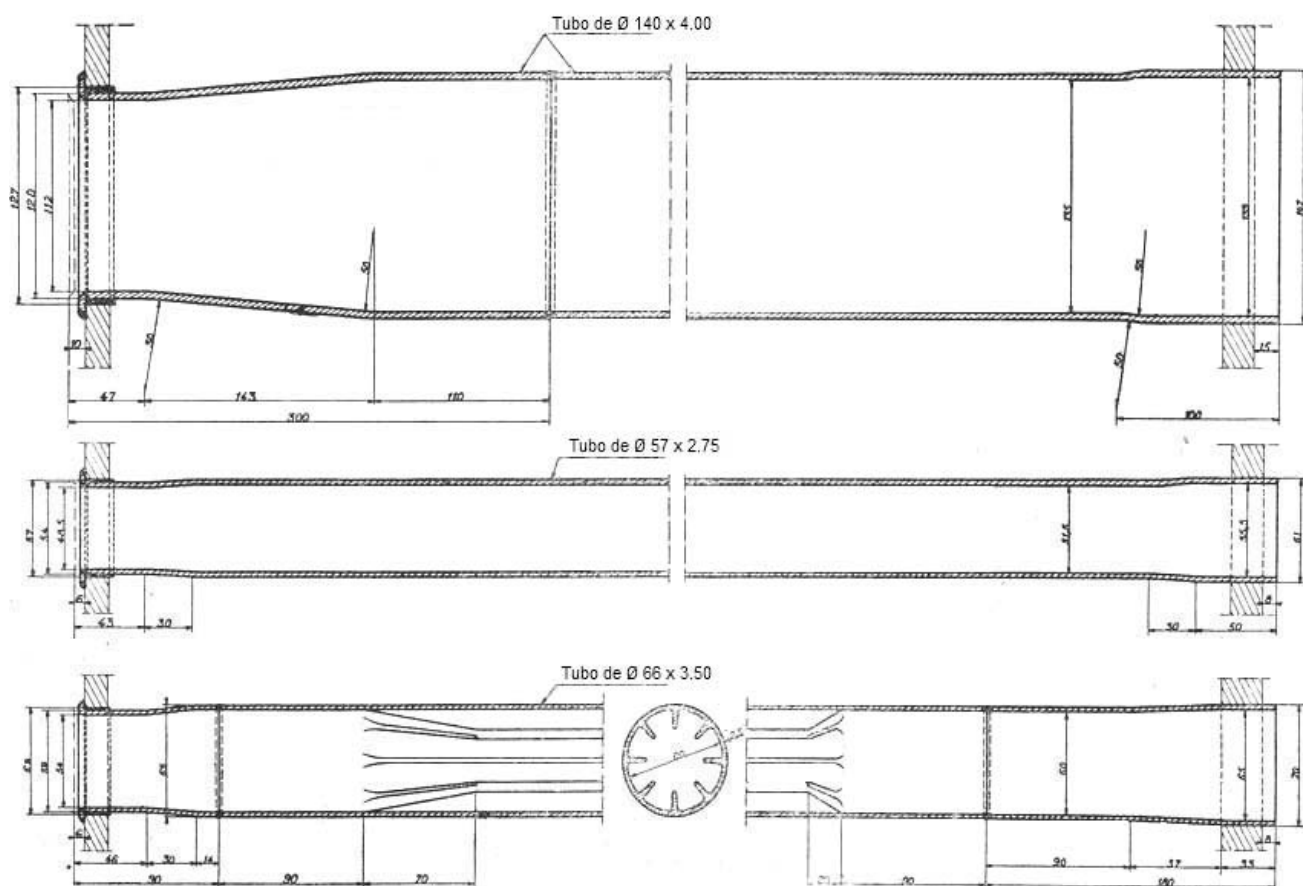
Montaje de los tubos en las placas tubulares de acero sobre las locomotoras de la S.N.C.F.
